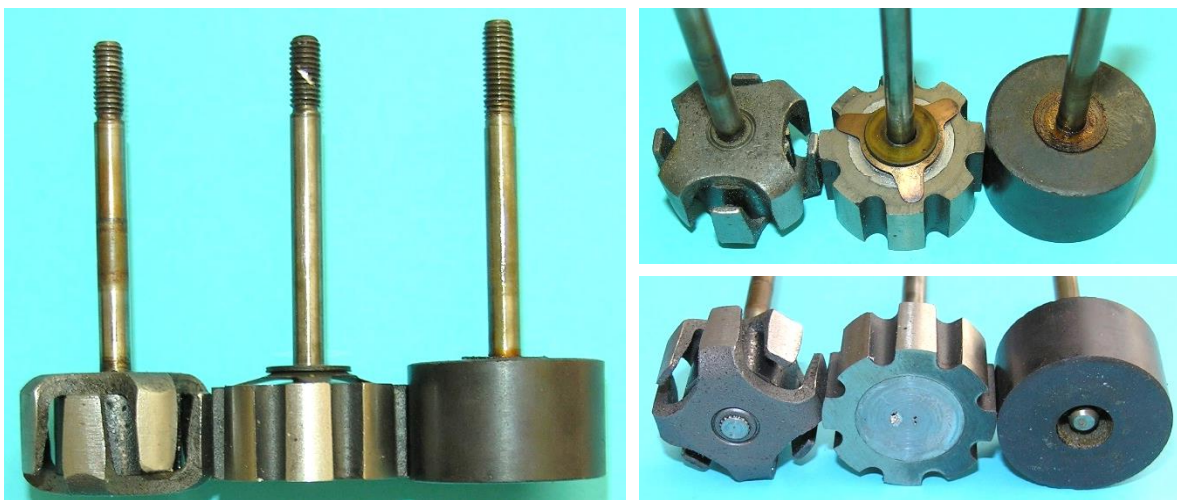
Ansichten der Polräder mit gleichen Durchmessern
